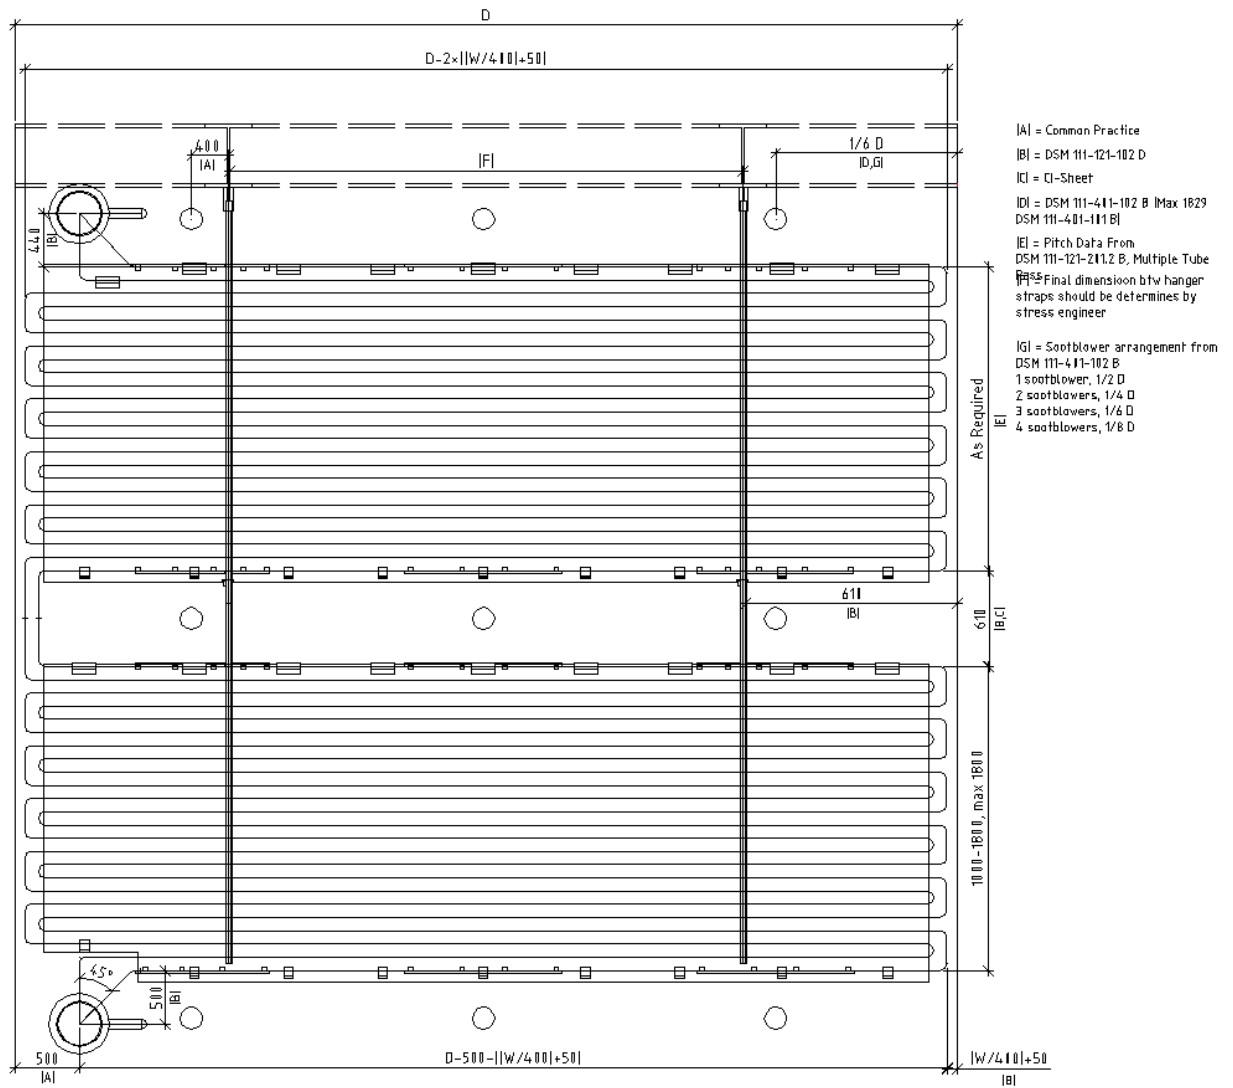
Single Tube Pass with hanger tubes (KauVo, muokatuilla outlet kammiolla)
